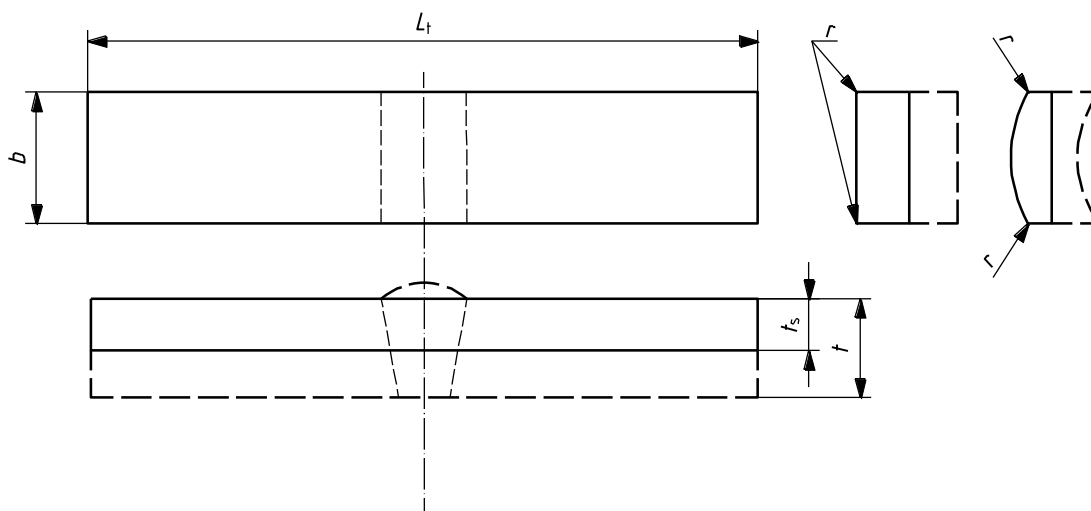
Поперечный образец для испытаний стыковых сварных швов на загиб с растяжением лицевой стороны (TFBB)
